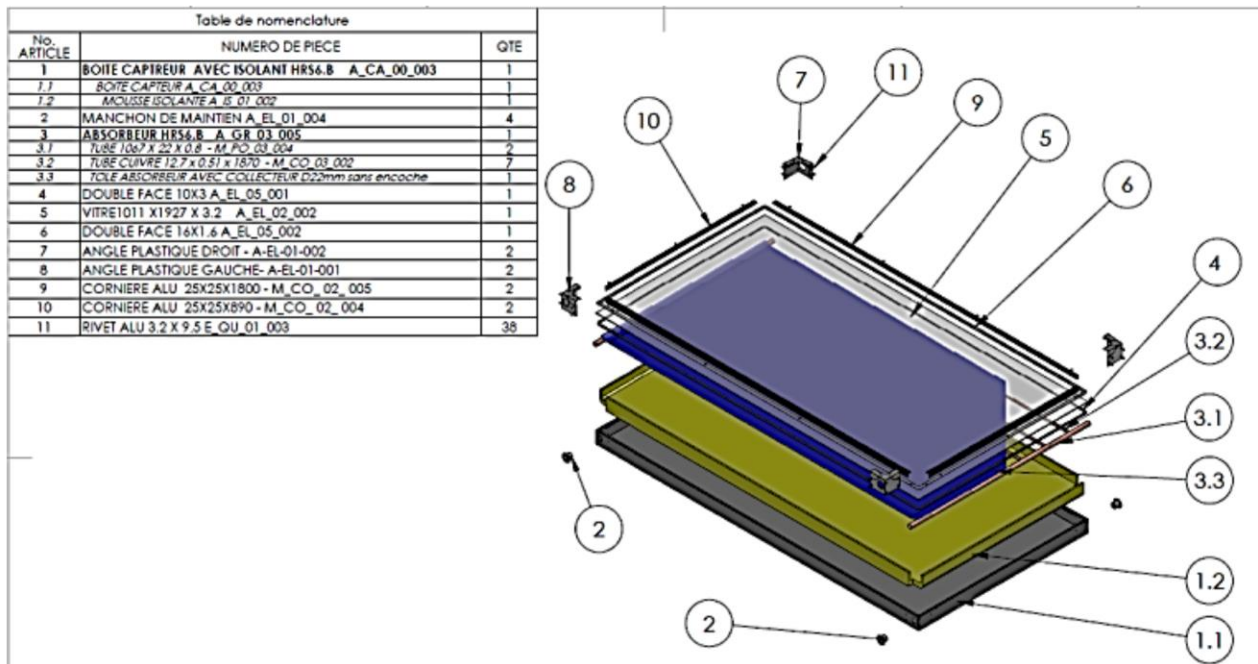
Vue éclatée du capteur (exemple pour le capteur HRS6 B)
